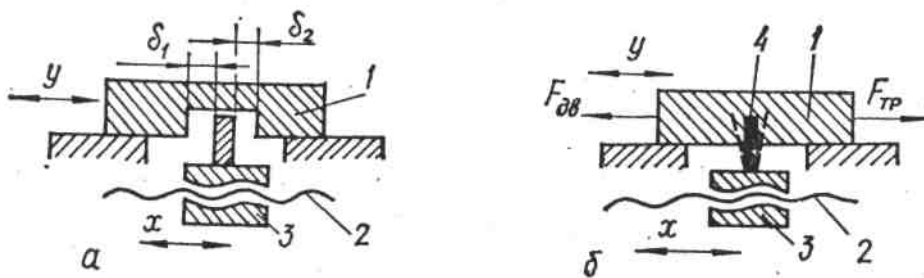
Кинематический зазор (а) и упругие отжатия (б) в приводе станка с ЧПУ
